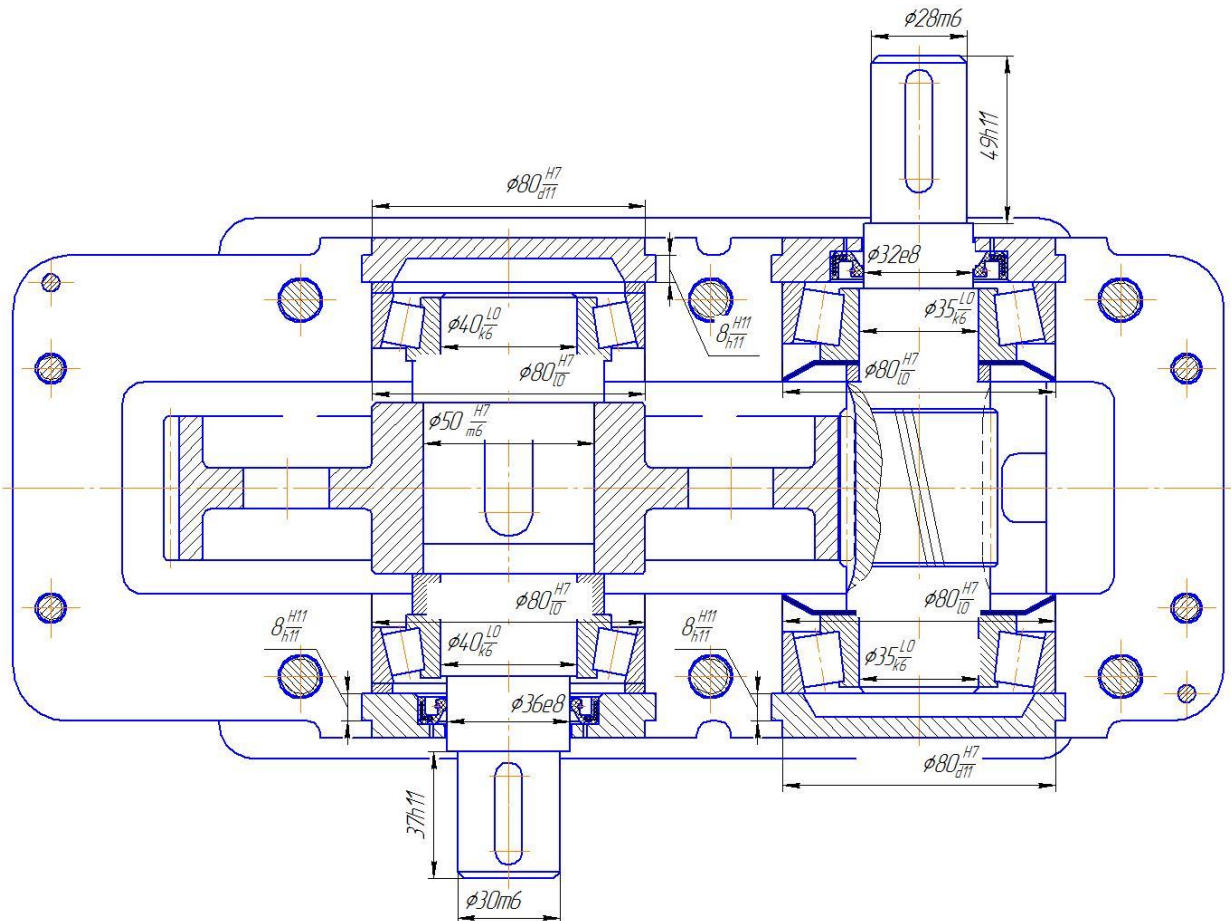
Складальне креслення редуктора барабанної лебідки
